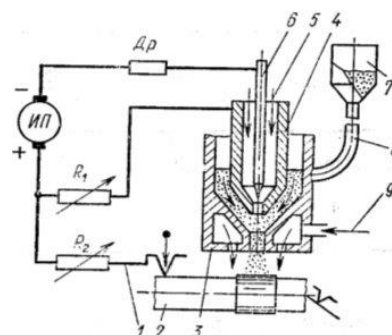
Восстановление изношенных валов наплавкой: 1-станок; 2-восстанавливаемый вал; 3-наружное сопло плазмотрона; 4- медное сопло; 5- плазмообразующий газ; 6- вольфрамовый катод; 7- питатель для подачи порошка; 8- транспортирующий газ; 9-защитный газ; ИП- источник электрического питания; R1 и R2- реостаты; Др- дроссель.
